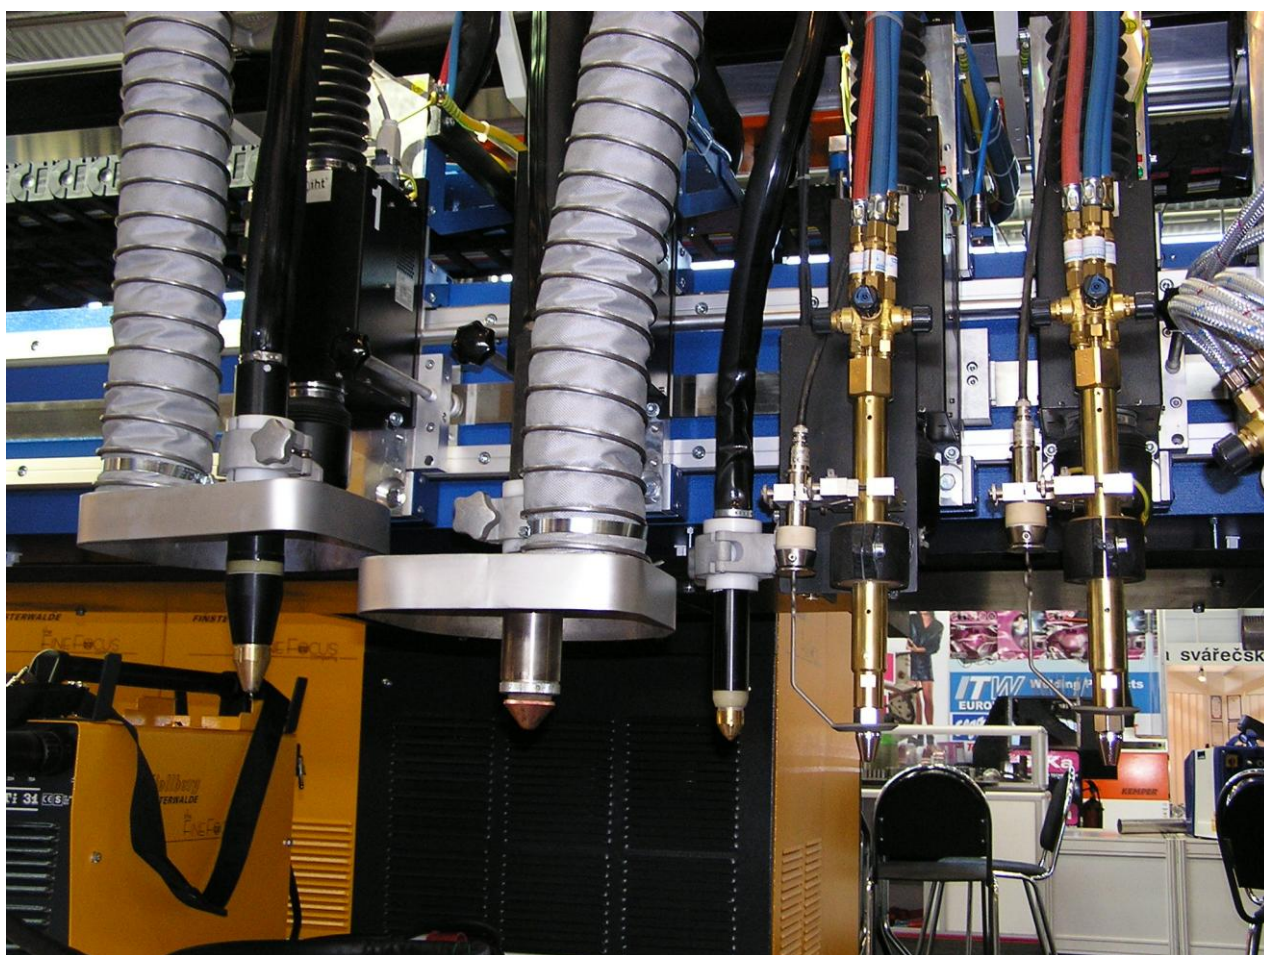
Řezání přesnou kyslíkovou plazmou
